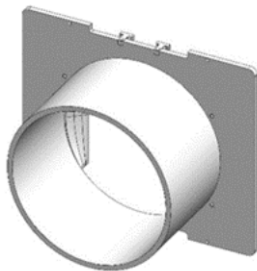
Plaque de connexion pré percée DN/OD 160 ou 315
